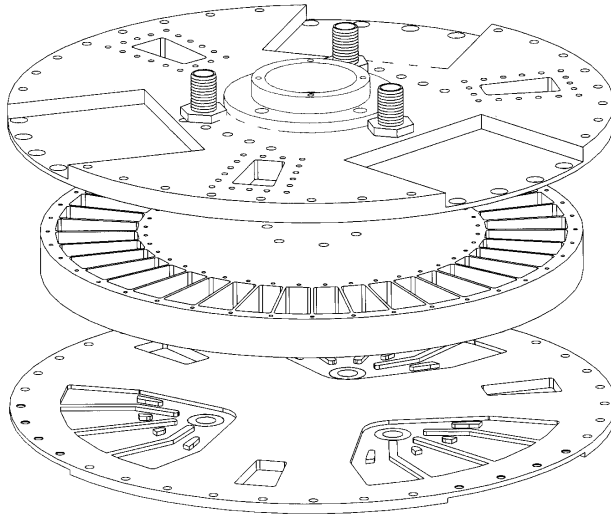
Explosionszeichnung der Gehäusedeckel und des Filterkarussells des Prototypen KMP3.
